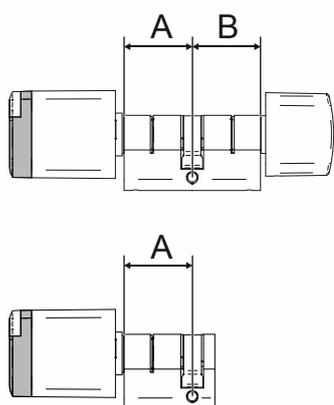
Запирающий цилиндр: ширина цилиндра с профилем EU
